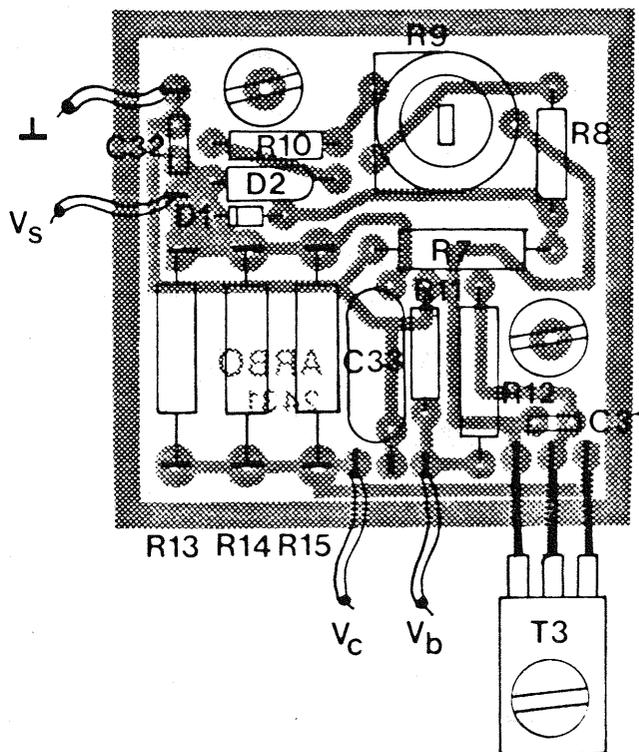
Circuito stampato per lo schema di fig. 7 visto dalla parte dei componenti
